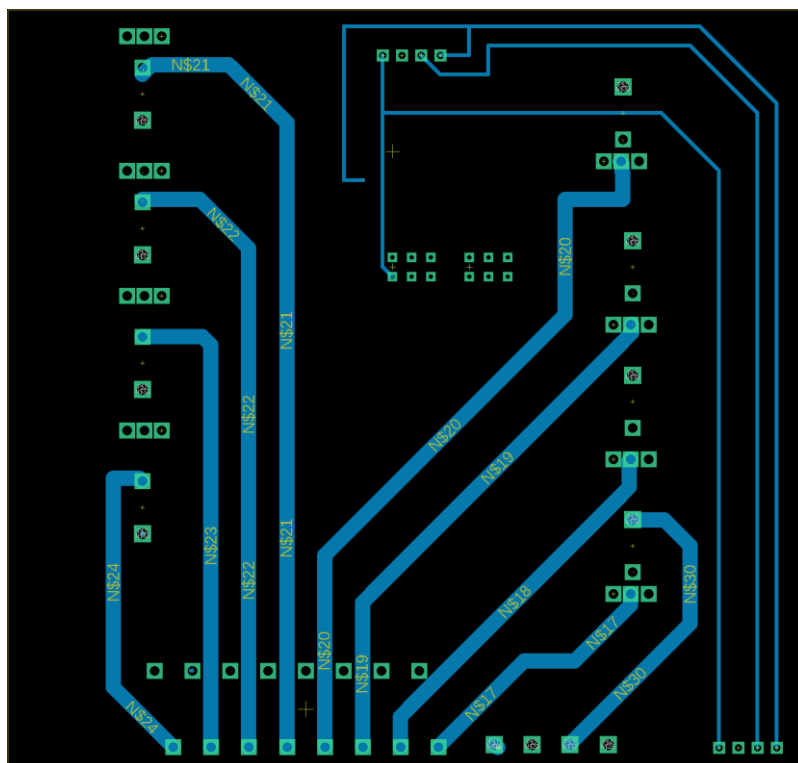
Placa salidas: Ruteo cara BOTTOM.
